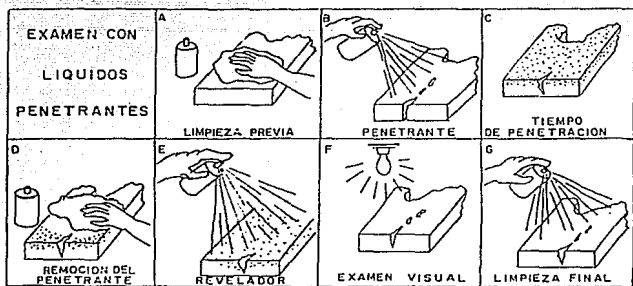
Pasos a seguir durante la inspección por líquidos penetrantes.
